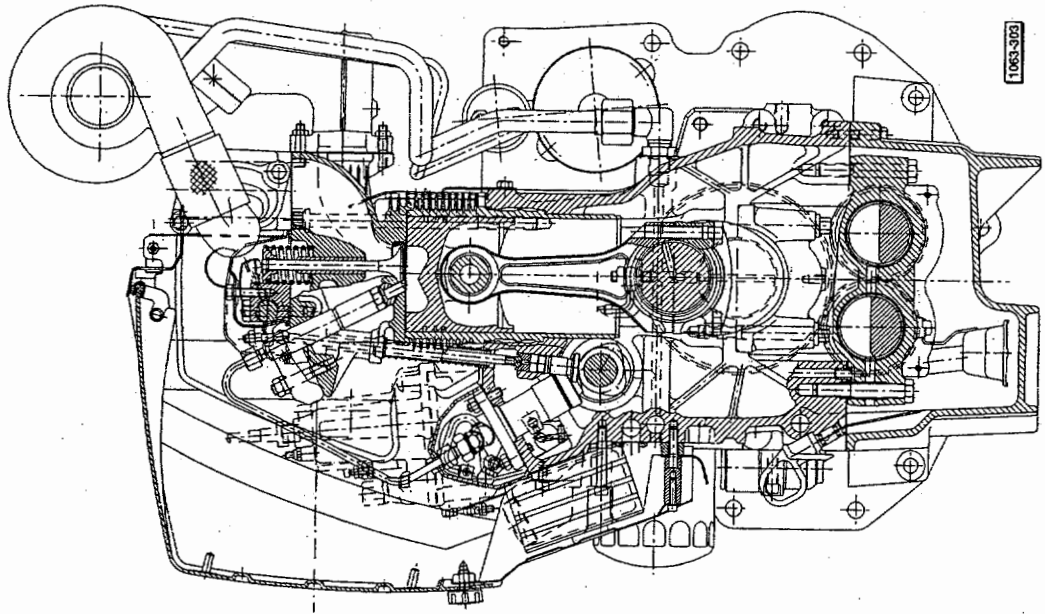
SILVER 90 - Coupe transversale du moteur - 4 cylindres
